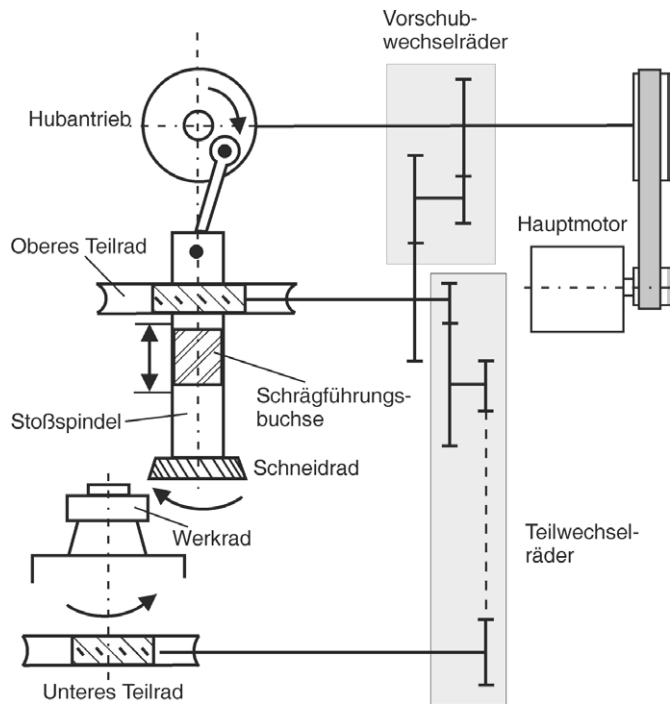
Getriebschema einer Wälzstoßmaschine
